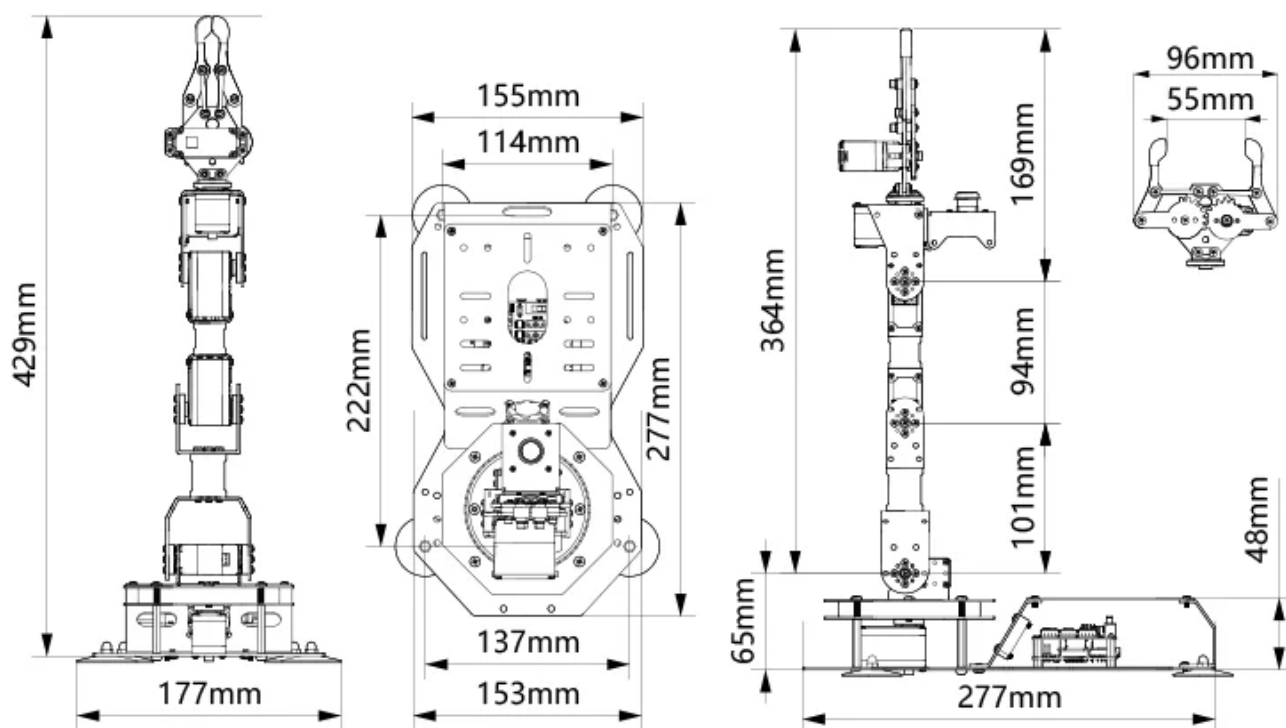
Габаритные чертежи робота-манипулятора AF.
